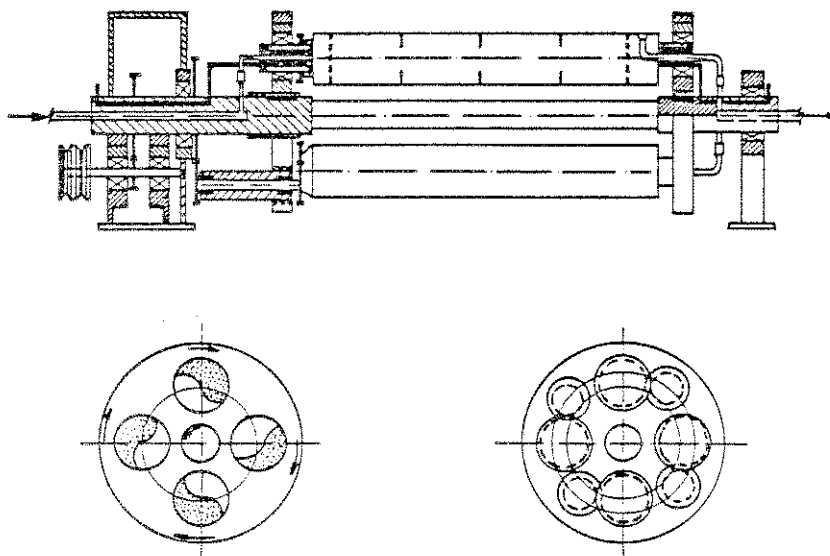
Prinzipskizze einer Planeten-Kugelmühle für Naßmahlung
